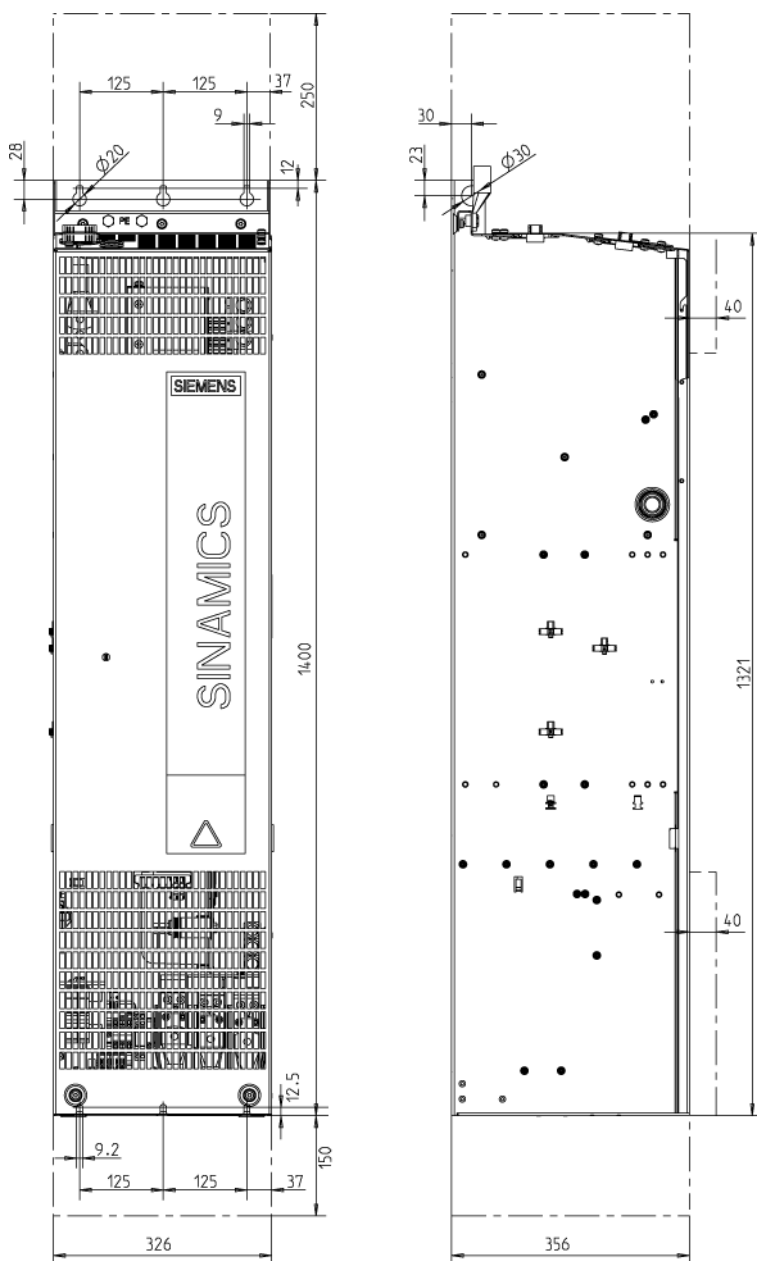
FX 型电机模块的外形尺寸图 正视图和侧视图
